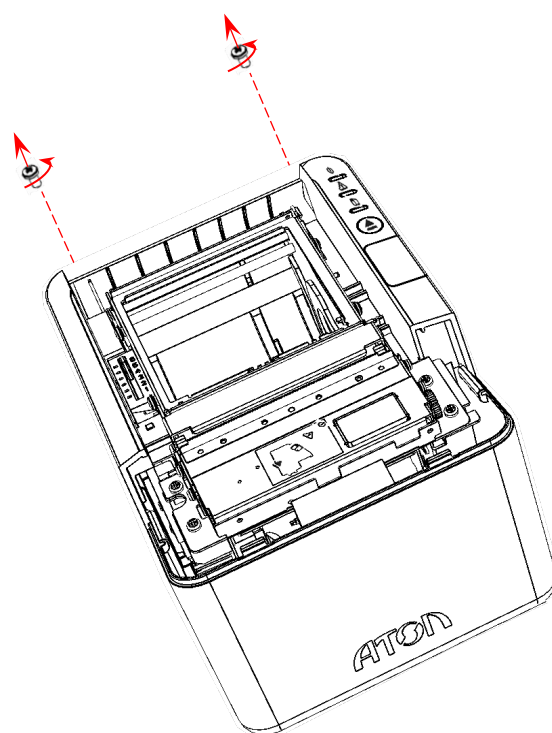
Винты крепления верхней части корпуса к печатающему механизму
